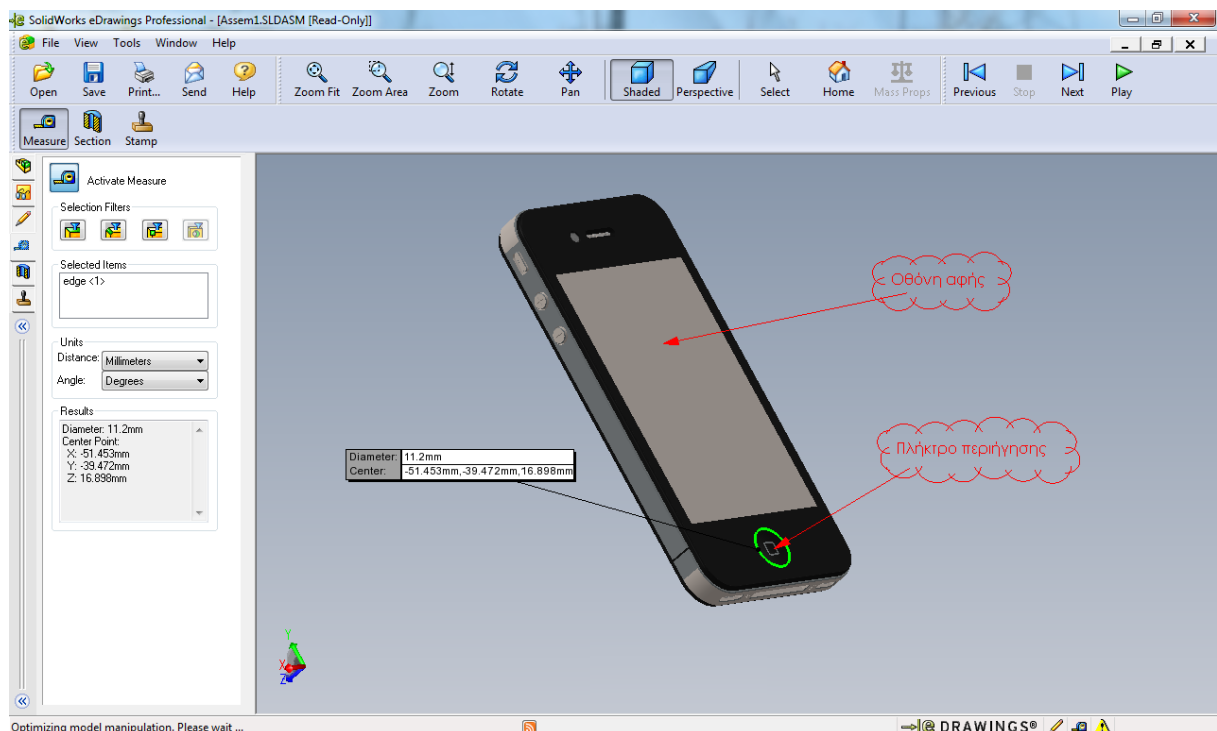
Ανάπτυξη σε 3D arrangement of parts and / or other assemblies.
